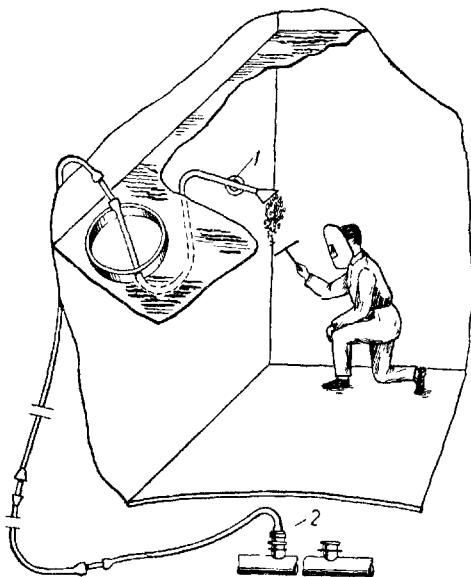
Отсос от сварочной дуги с помощью вакуум-насосной установки
